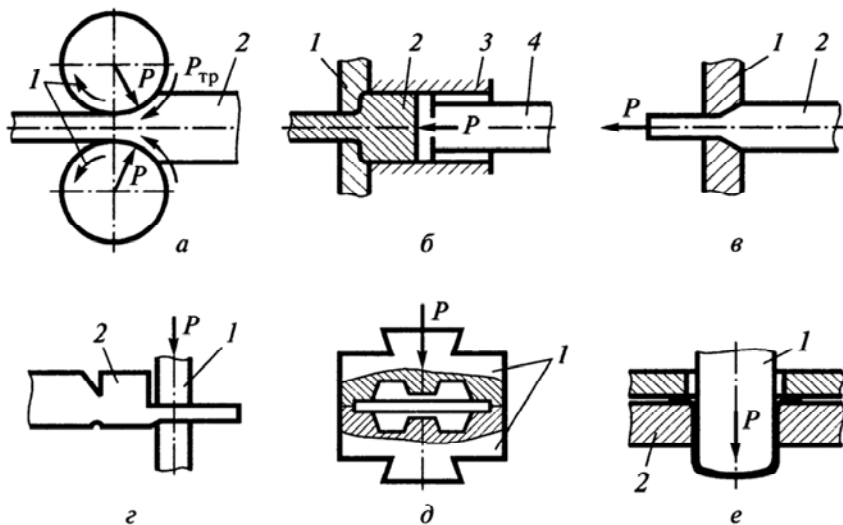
Схемы основных видов обработки металлов давлением: а – прокатка; б – прессование; в – волочение; г – свободная ковка; д – объемная штамповка; е – листовая штамповка
